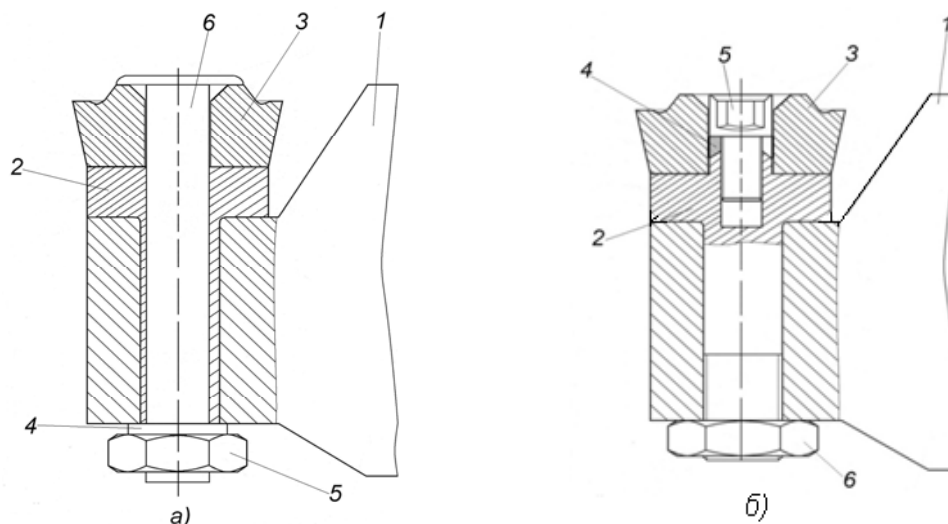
Базовая (а) и усовершенствованная (б) конструкции сборного чашечного резца
